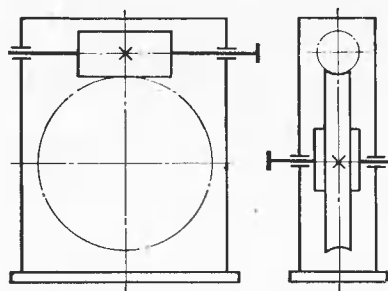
Кинематическая схема червячного редуктора с верхним расположением червяка
